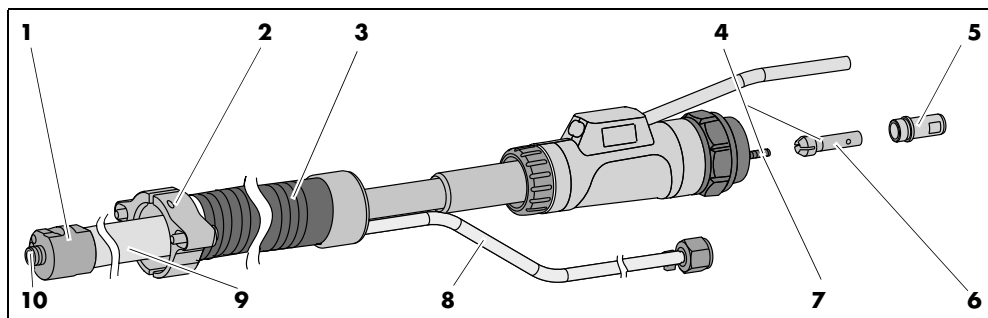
Ersatzteilliste Schlauchpaket / Hose assembly ABIROB® A
